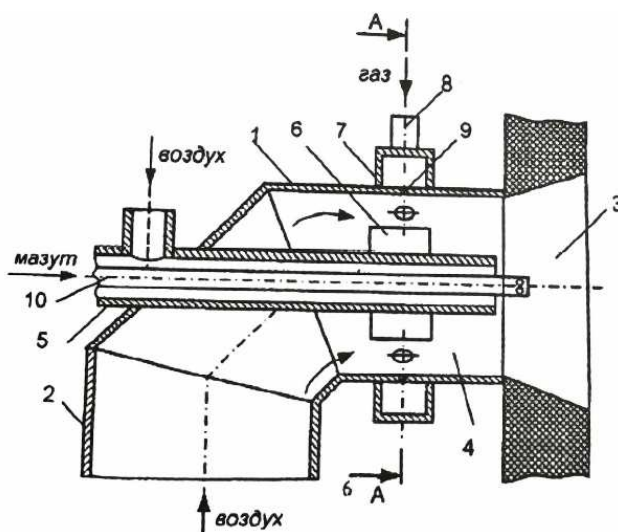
Новая малотоксичная горелка типа ГП-2 конструкции ДВГУПС
